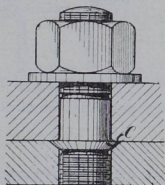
Stiftschrauben mit Bund zum Verstemmen.
